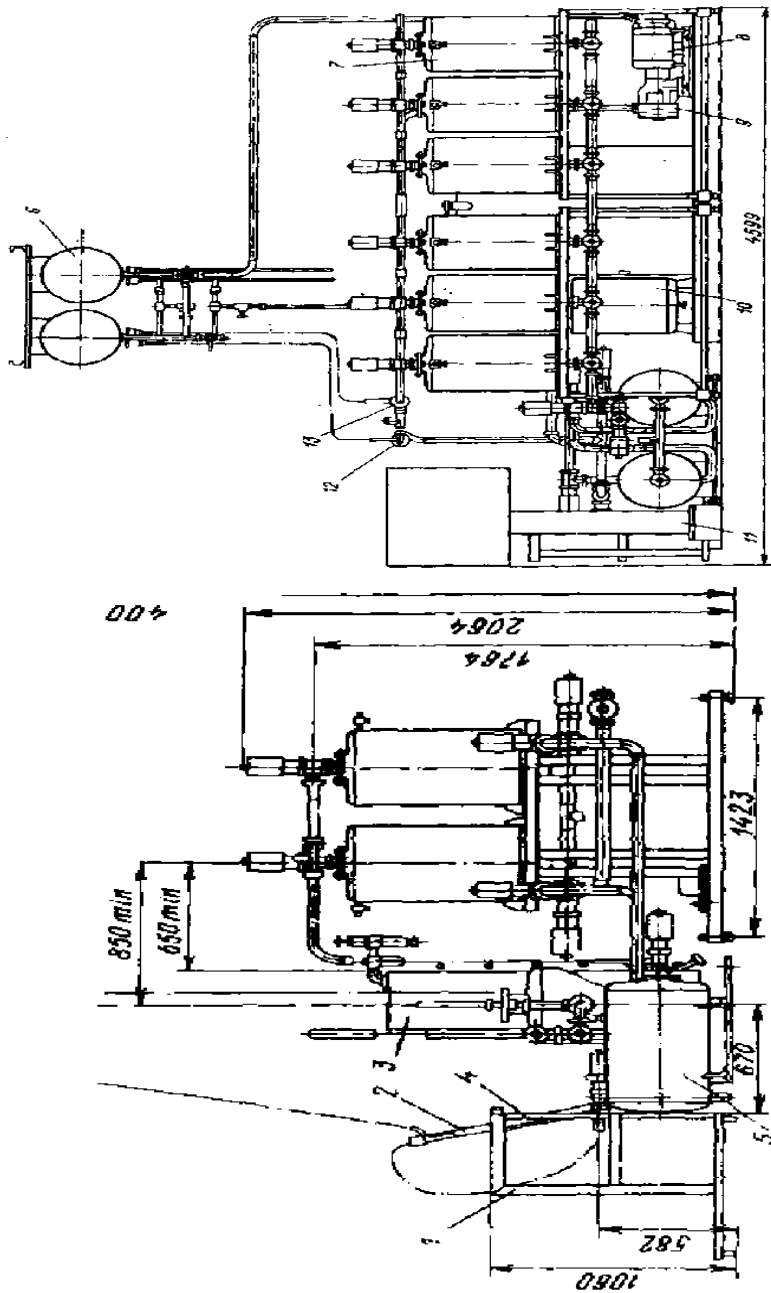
Схема установки В2-ФВУ-100 для сбора пищевой крови:
